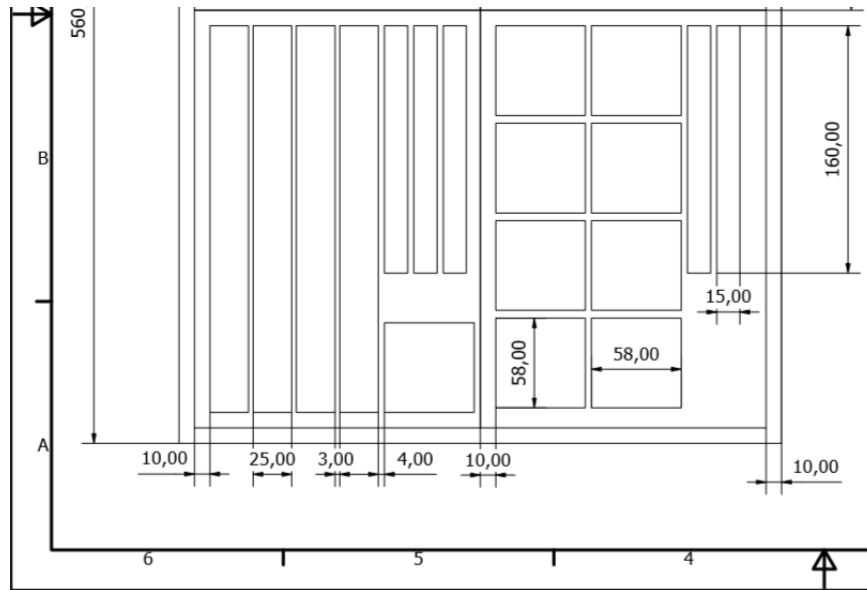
Plano de tablero de las probetas de tracción, flexión e impacto
